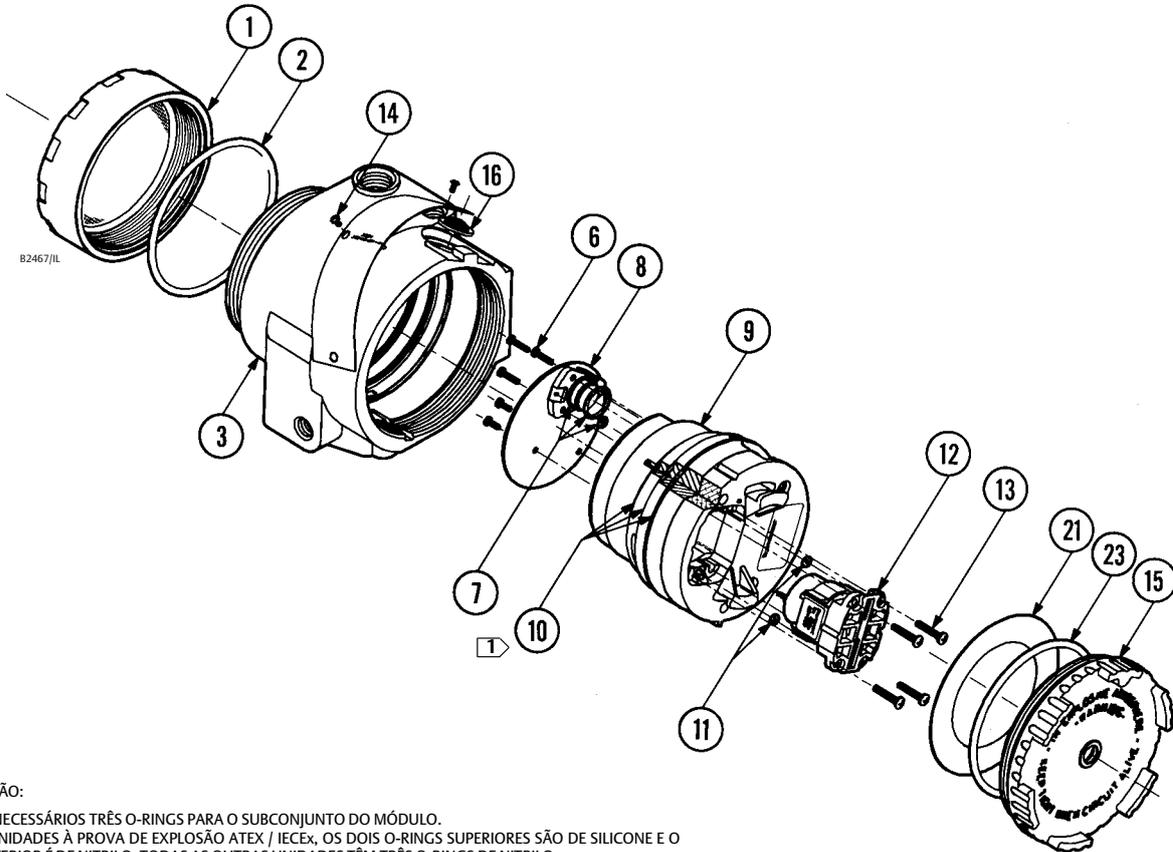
Desenho de peças explodidas (consulte também a tabela 7-2)
